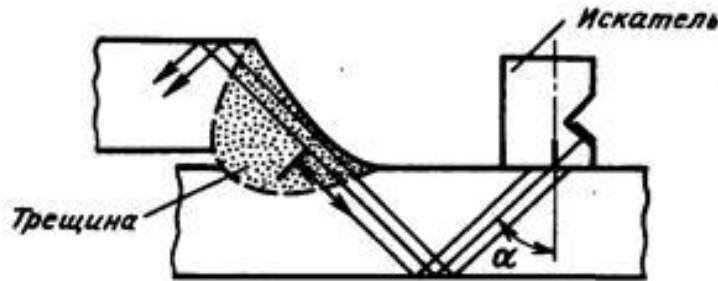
Схема УЗ-контроля сварного соединения внахлестку с трещиной в шве
